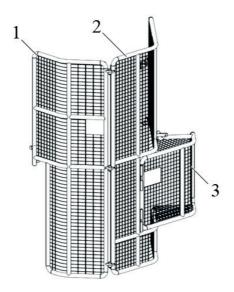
Кожух для защиты от вращения штанг: 1 – левый кожух; 2 – правый кожух; 3 – удлинитель кожуха
